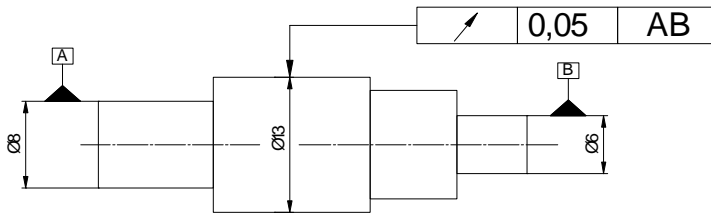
Şekil ve Konum Toleranslarının Gösterilme Standardı (Devam)
